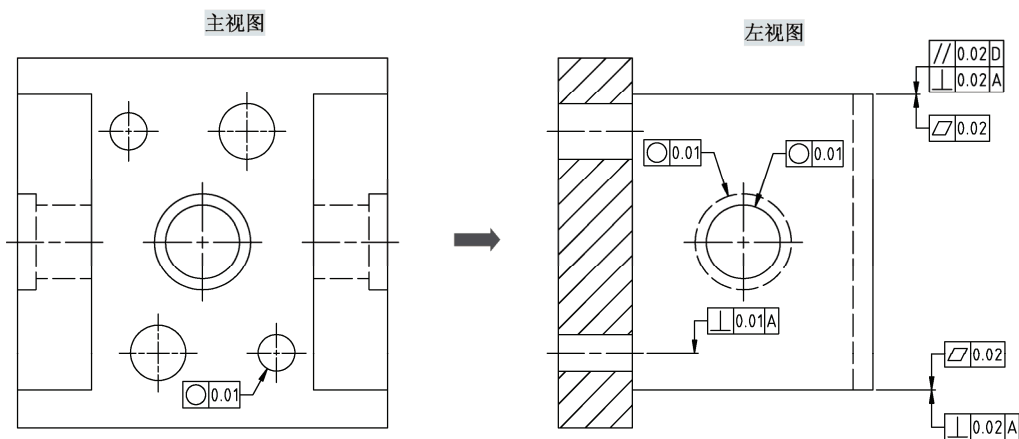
“主视图”和“左视图”形位公差标注
